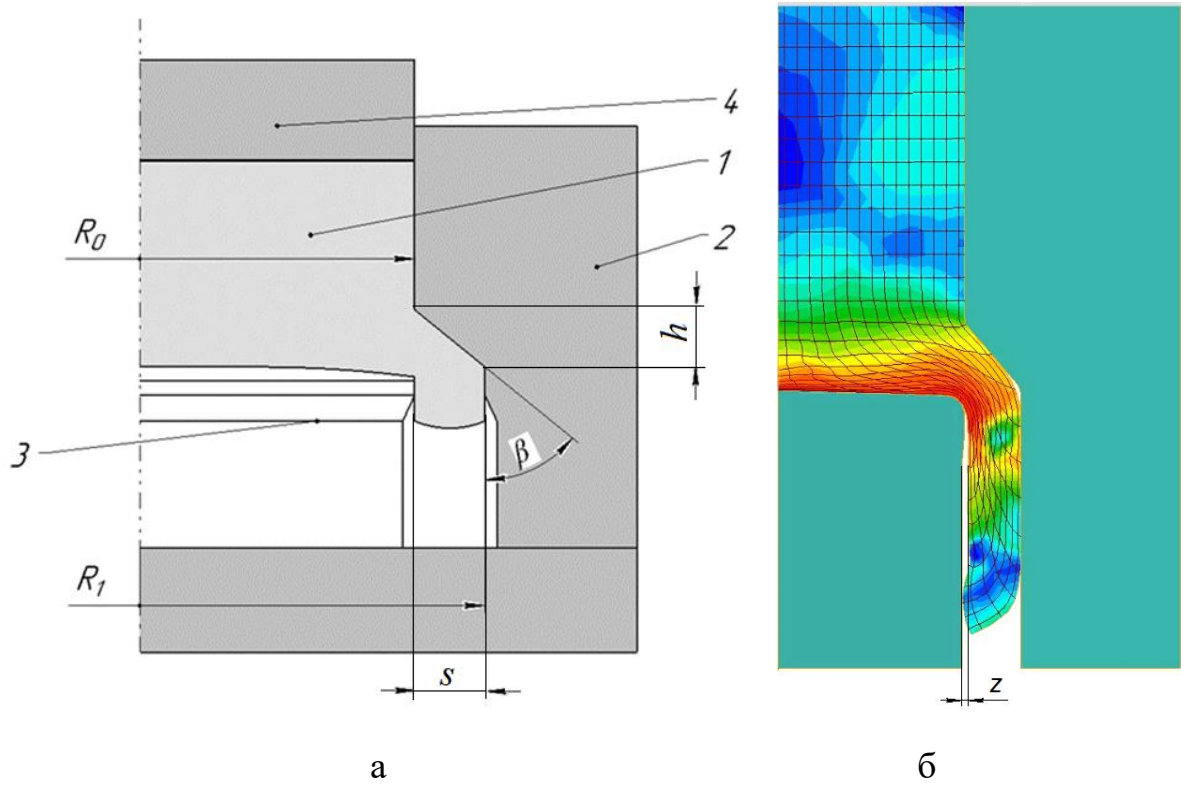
Схема початкової стадії процесу видавлювання з роздачею (а) і контур видавленої деталі (б)
